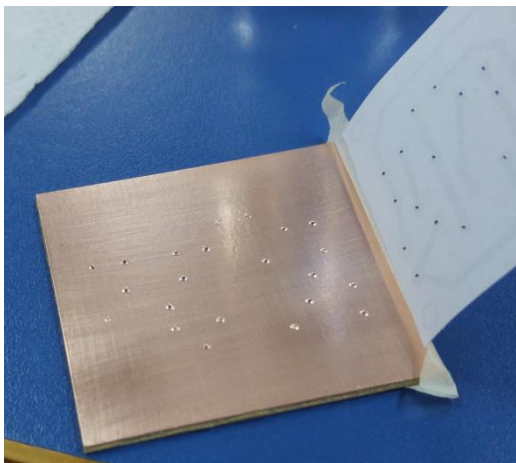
Retirar el Modelo Fijado sobre el PCB
